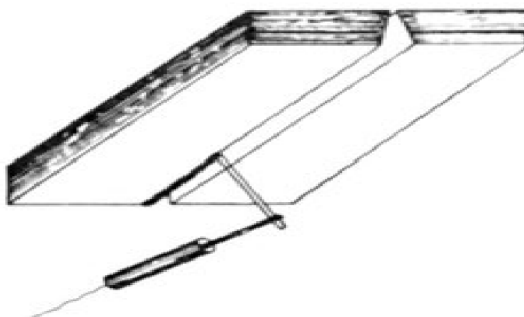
Posición sobre cabeza de soldadura.
